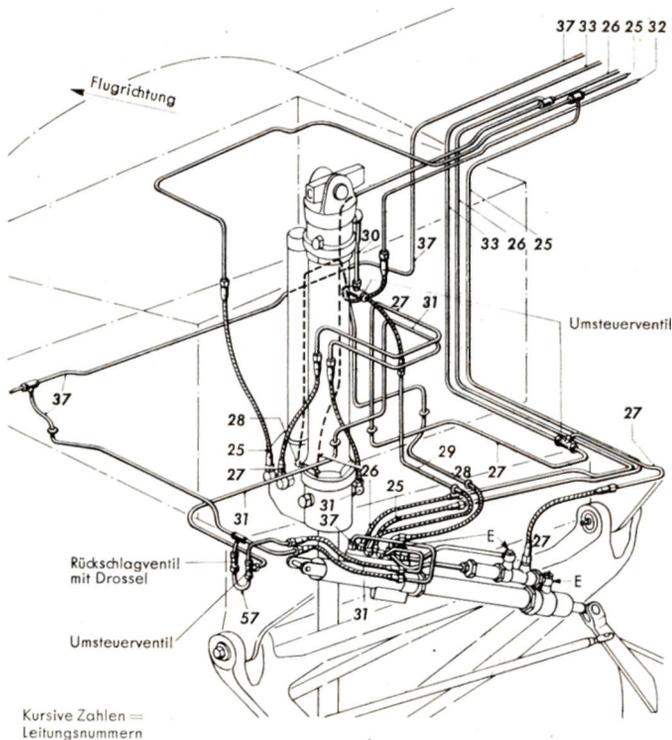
Drucköl-Leitungen der Fahrgestellstrebe und Fahrgestellklappenstrebe, links
